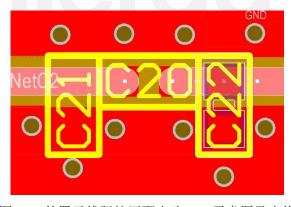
外置天线阻抗匹配电路 PCB 示意图及走线说明
